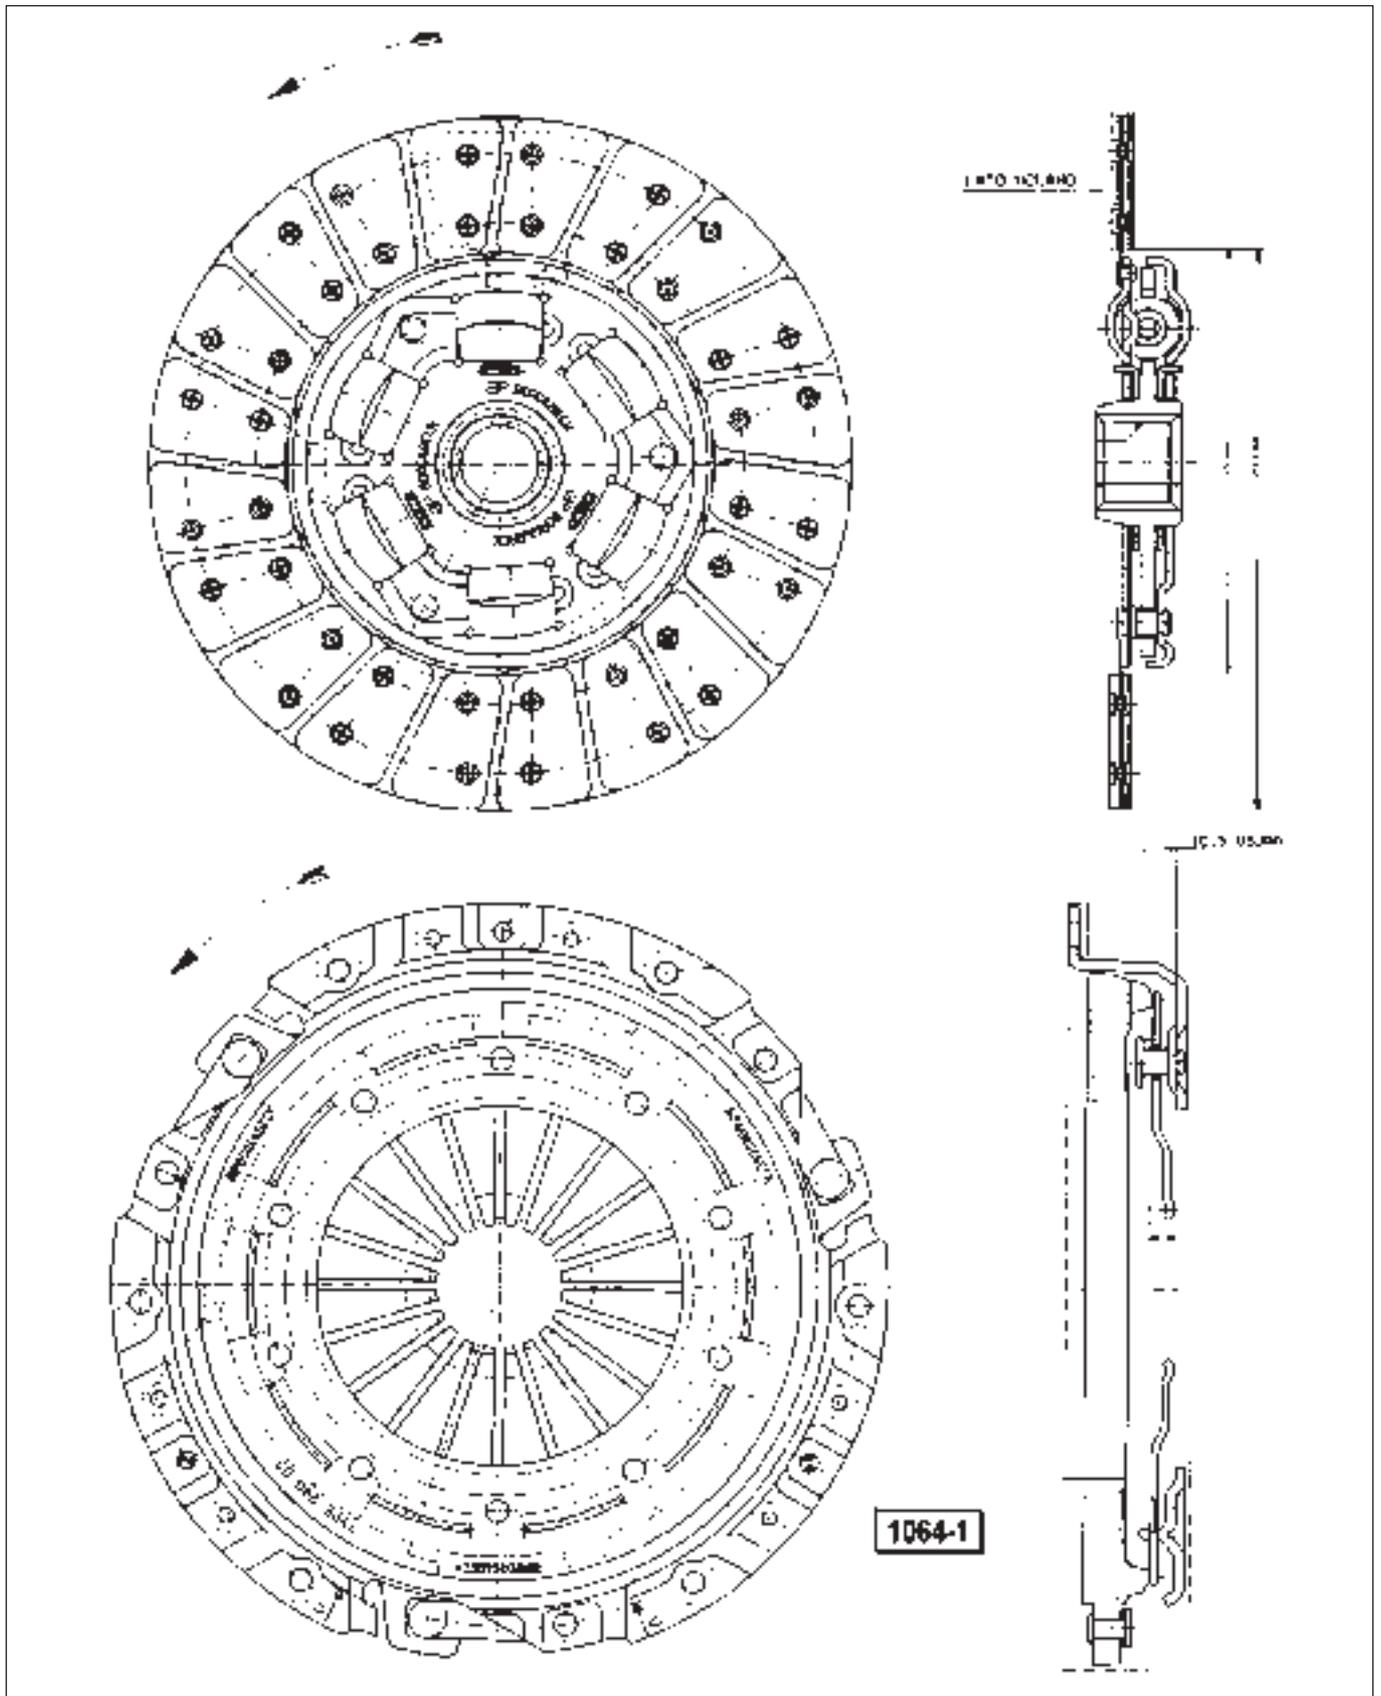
Vue d'ensemble de l'embrayage pour AGROPLUS 60
